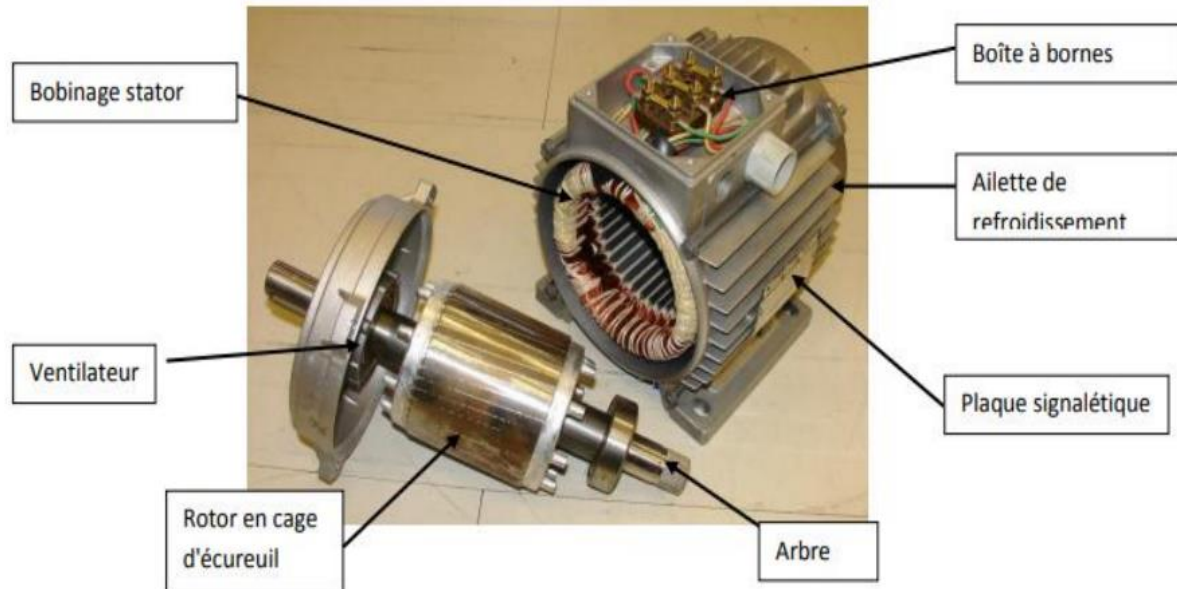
Rotor et Stator de Machine Asynchrone
